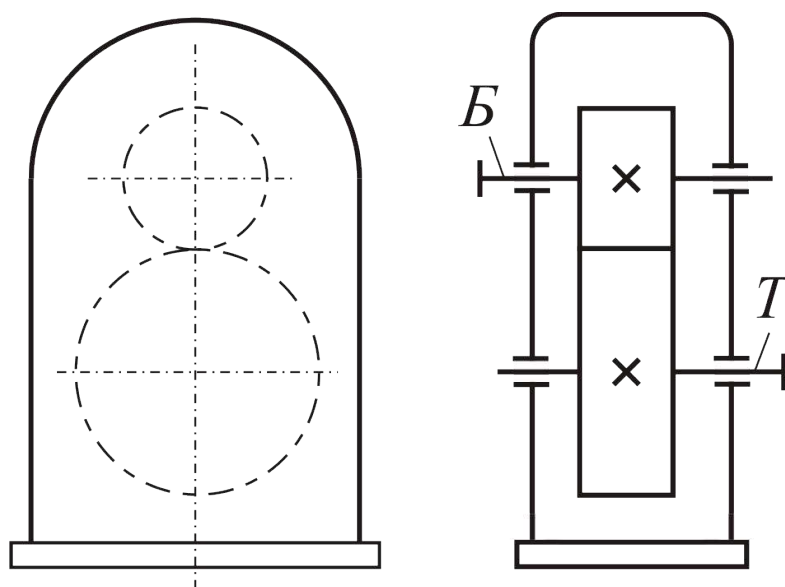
Кинематическая схема одноступенчатого вертикального редуктора с цилиндрическими колёсами
